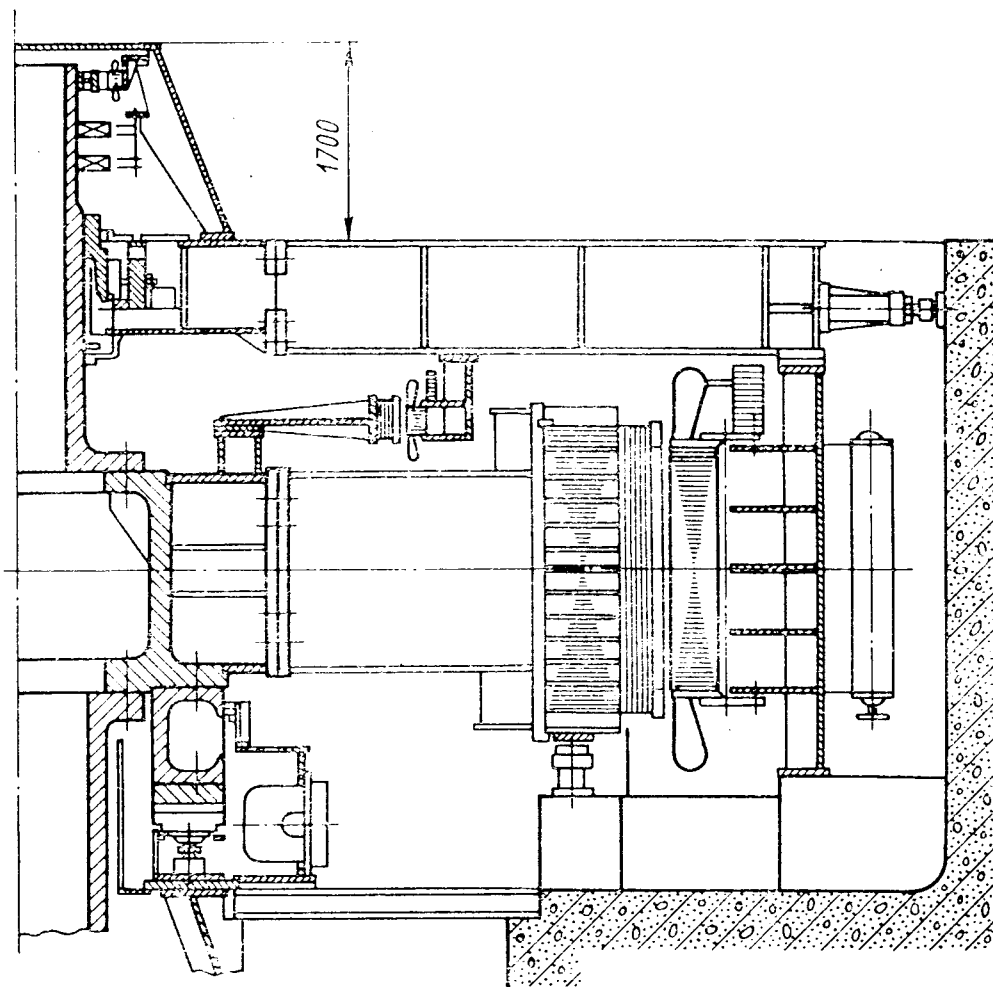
Гидрогенератор зонтичного исполнения. Сборочный чертеж
